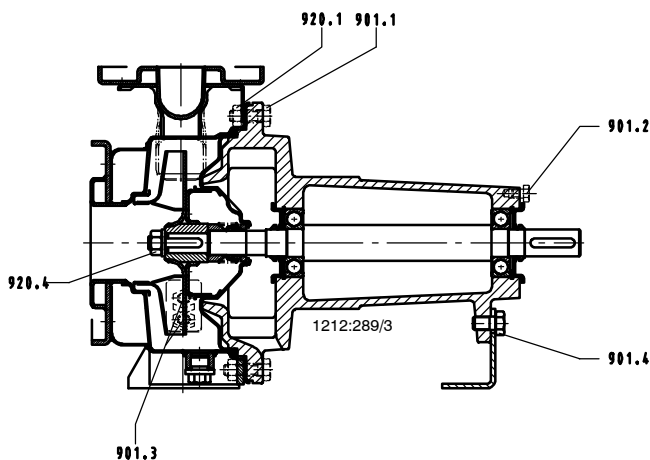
Места затяжки резьбовых соединений Etachrom NC с диаметром рабочего колеса 125, 160, 200, за исключением 50-200, 65-200, 80-200
